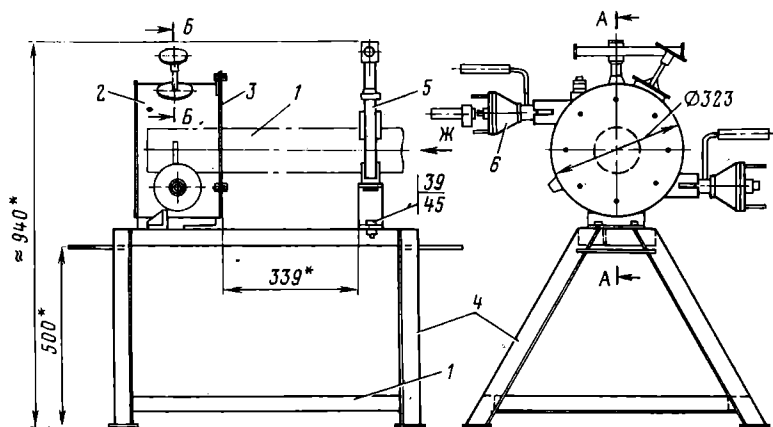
Установка для отжига концов труб перед вальцовкой:
